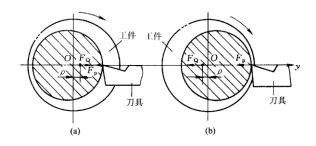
6 切削力作用点位置变化引起的加工误差 图 6-7 零件形状误差的复映
